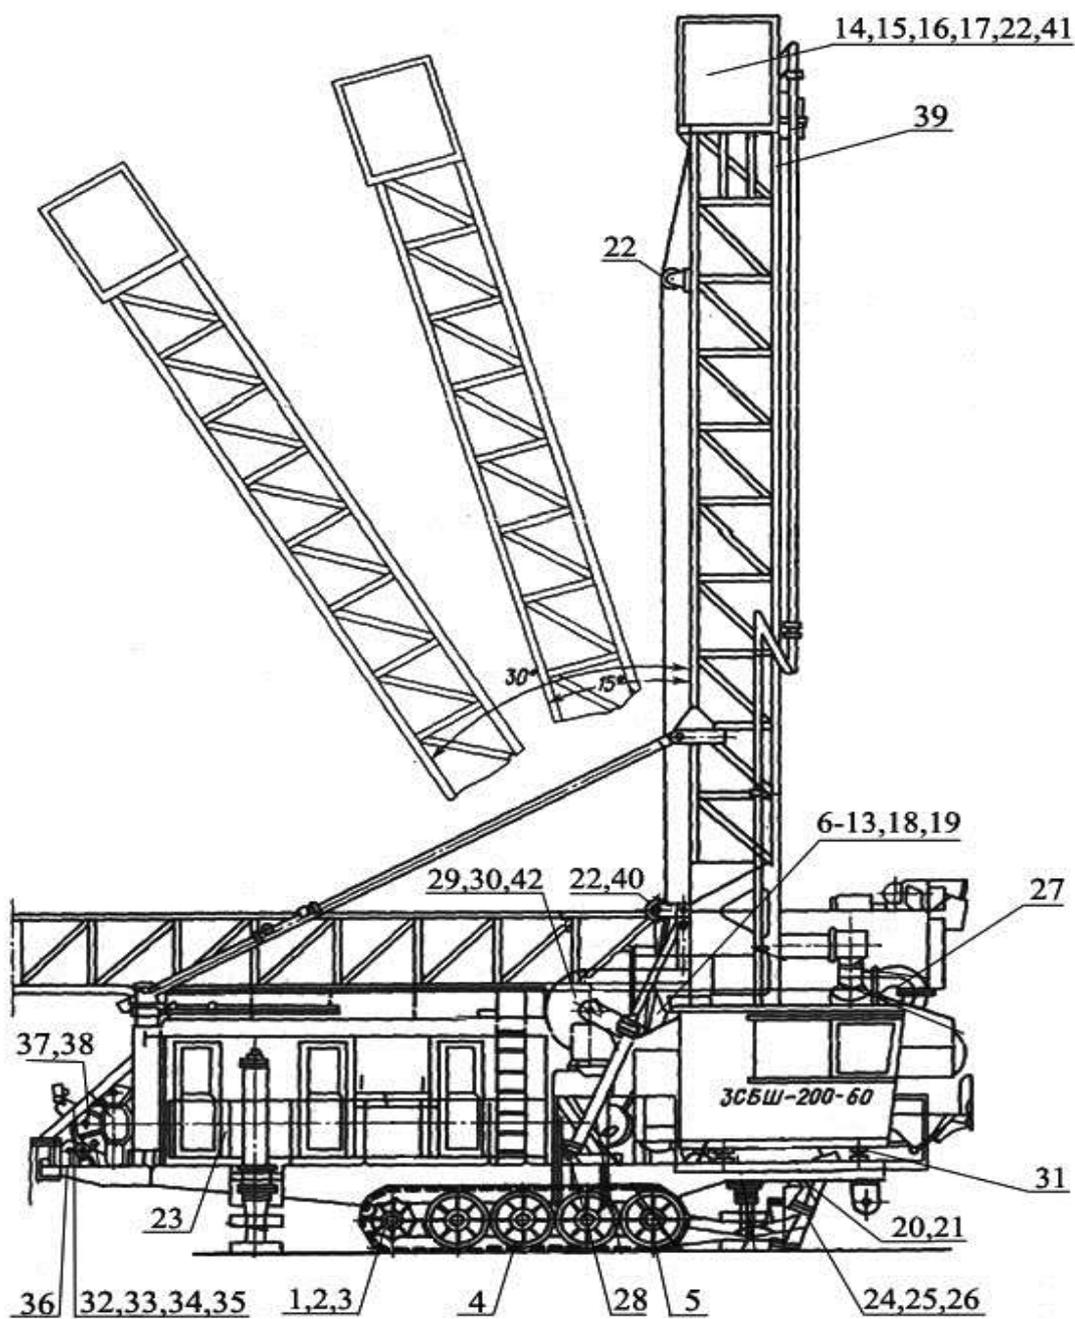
Схема смазки карьерного бурового станка ЗСБШ-200-60
